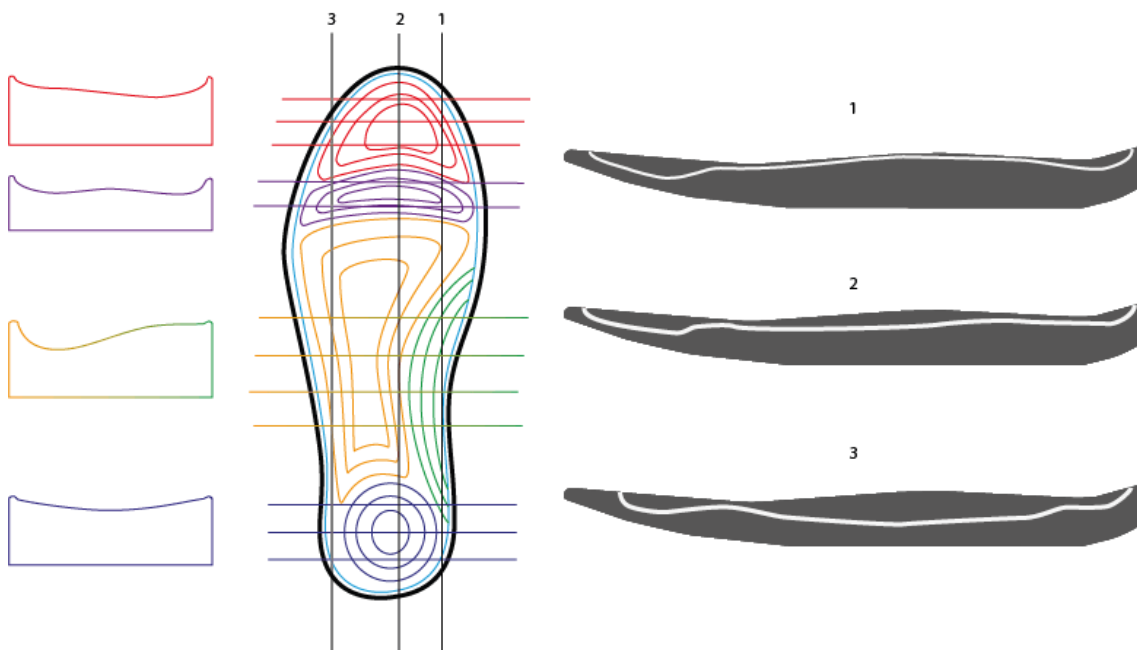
Planos y cortes de perfil y alzado de la entresuela
